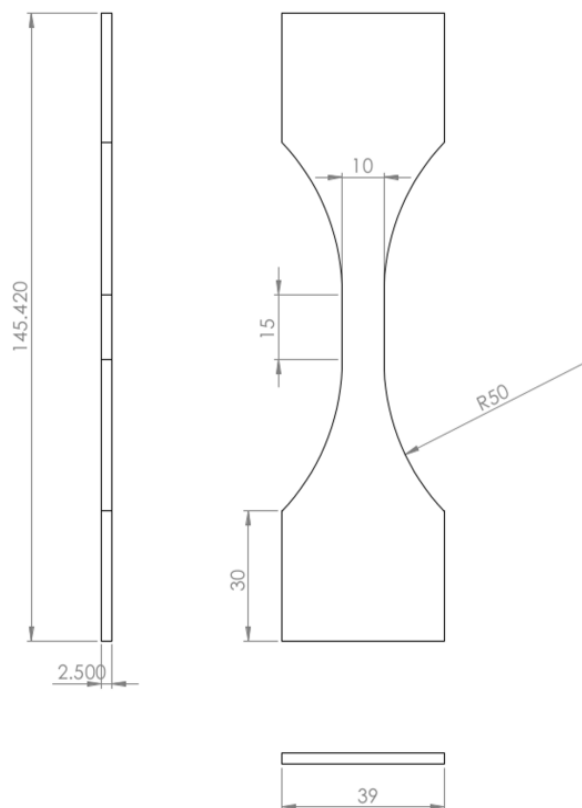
Géométrie de l'éprouvette de fatigue pour le chargement de traction uniaxiale
